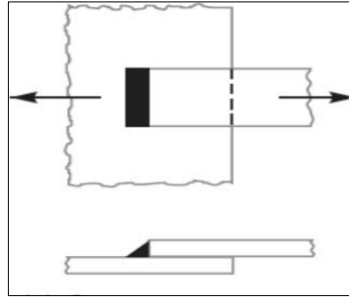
सिंगल ट्रान्सव्हर्स फिलेट (Single transverse fillet weld)
